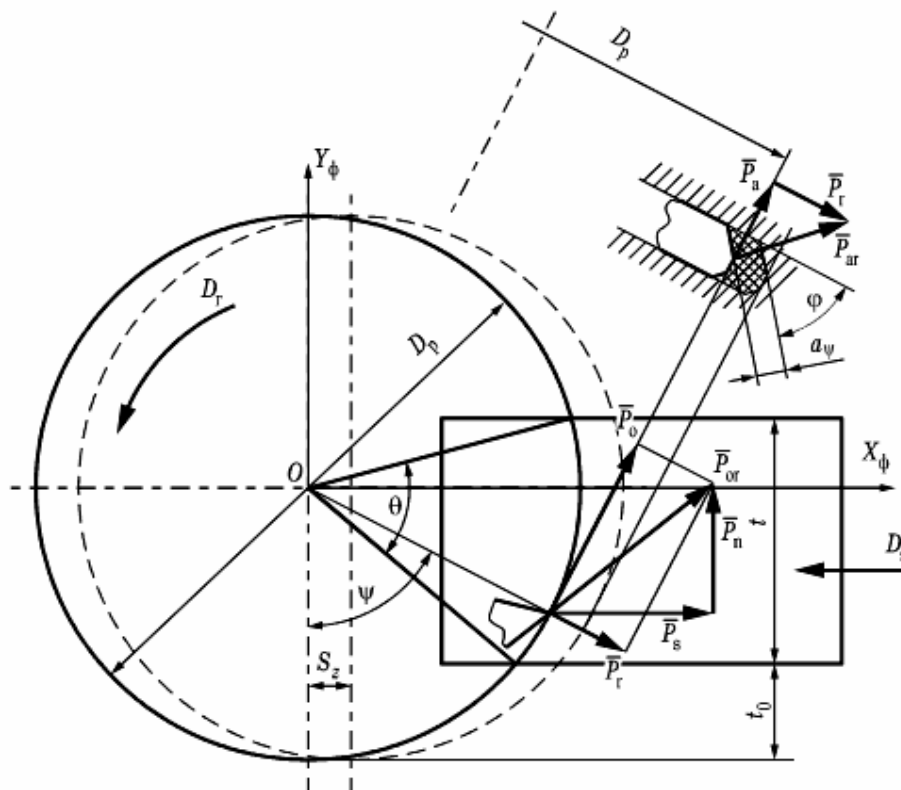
Схема дії сил на зубці при фрезеруванні дисковою фрезою
